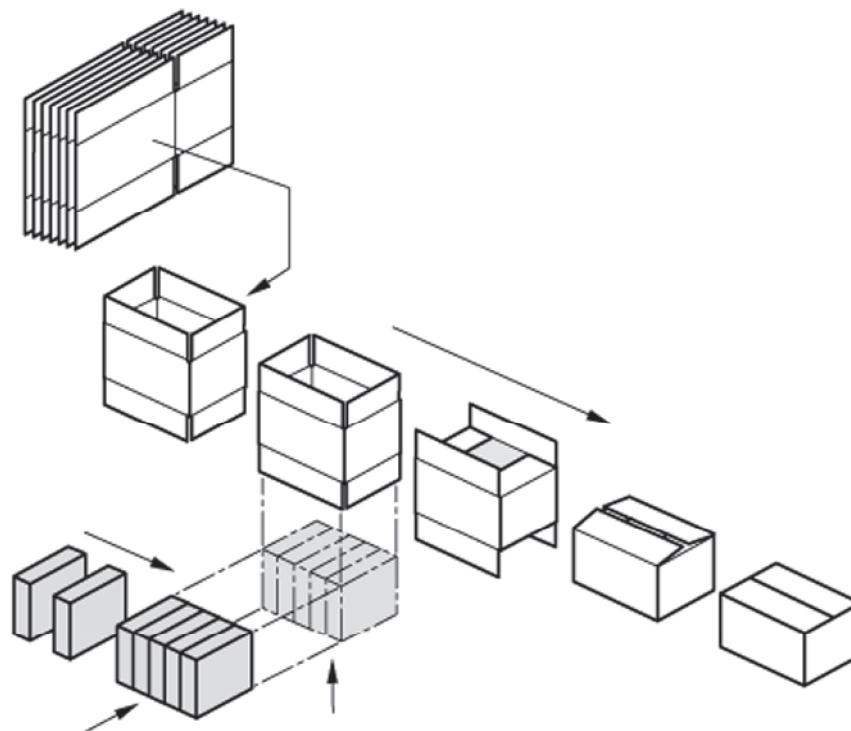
Faltschachtelverpackungsmaschine mit Zuführung von unten
